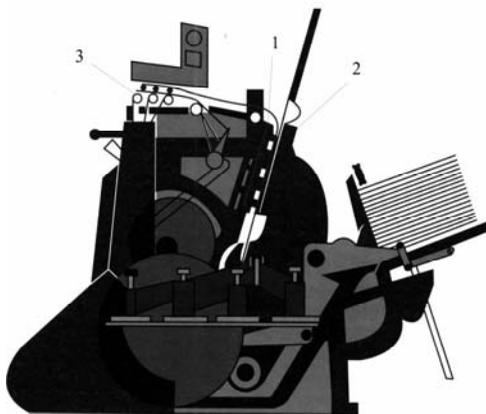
Схема тигельного прессы для тиснения фольгой фирмы Steuer: *1* — качающаяся плита (тигель); *2* — неподвижная плита (талер); *3* — штамп
